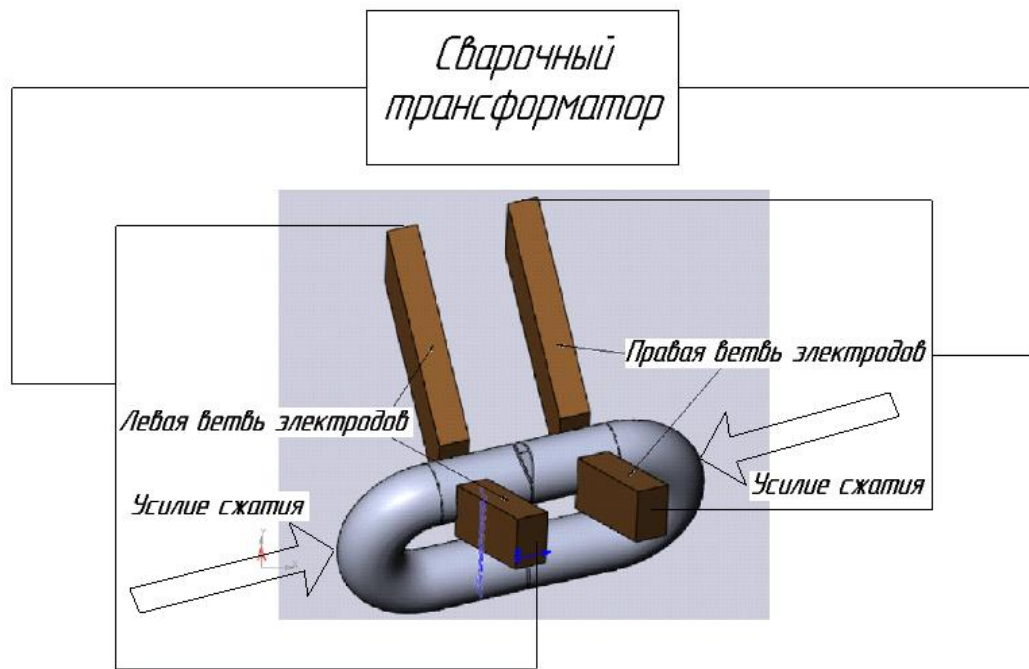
Принципиальная схема сварки круглозвенных цепей
